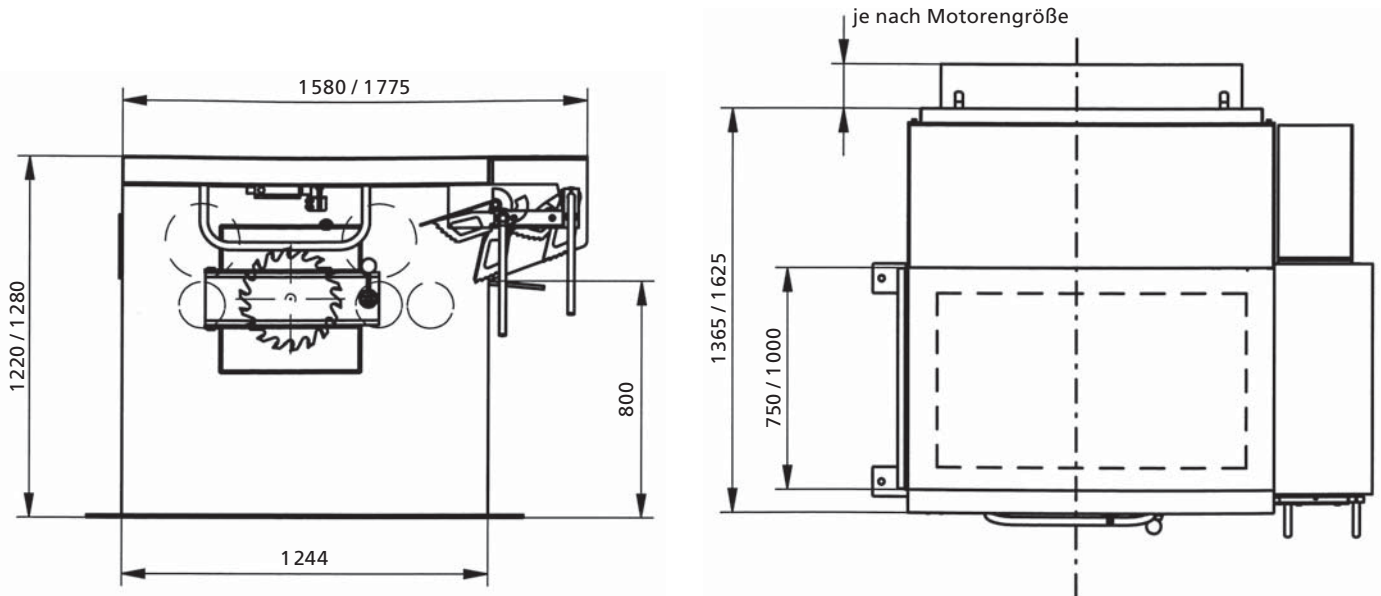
Maschinenabmessungen (mm) einer KME2/BM
